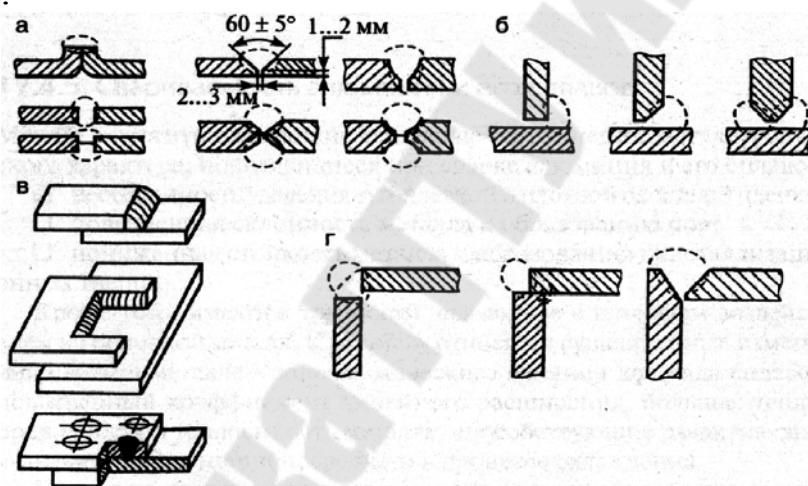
Типы сварных соединений: а – стыковое; б – тавровое; в – нахлесточное; г – угловое
